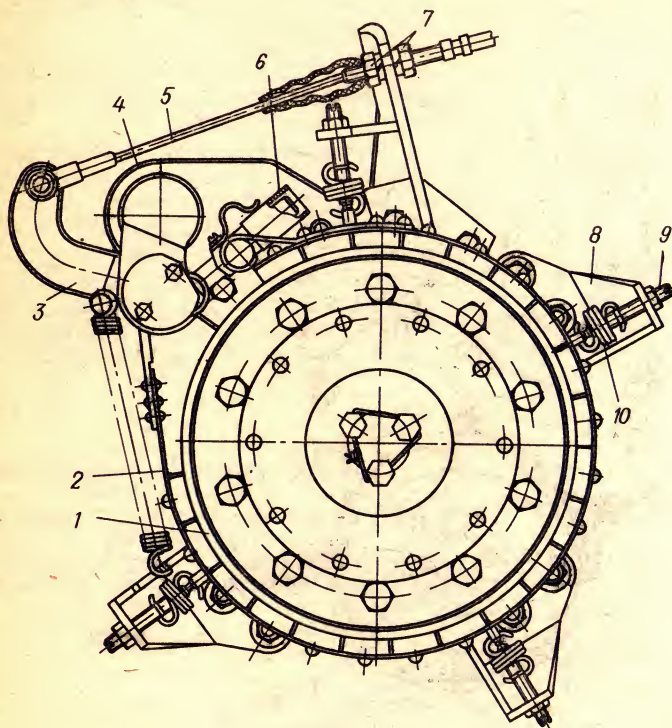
Ручной (стояночный) тормоз тракторов К-701 и К-700А: 1 — тормозной барабан; 2 — тормозная лента; 3 — рычаг; 4, 8 — кронштейн; 5 — трос; 6 — регулировочная гайка; 7 — гайка; 9 — регулировочный винт; 10 — оттяжная пружина
